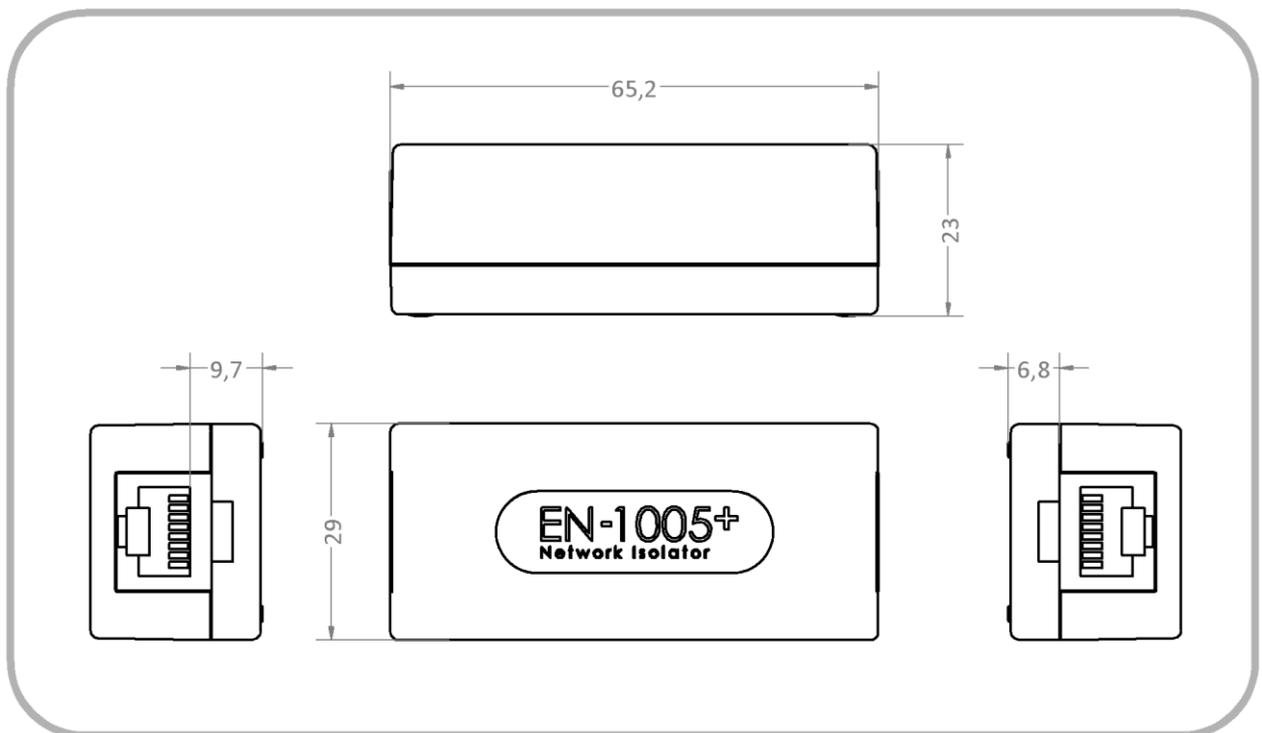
Maßzeichnung EN-1005+. Alle Maßangaben in Millimetern.
